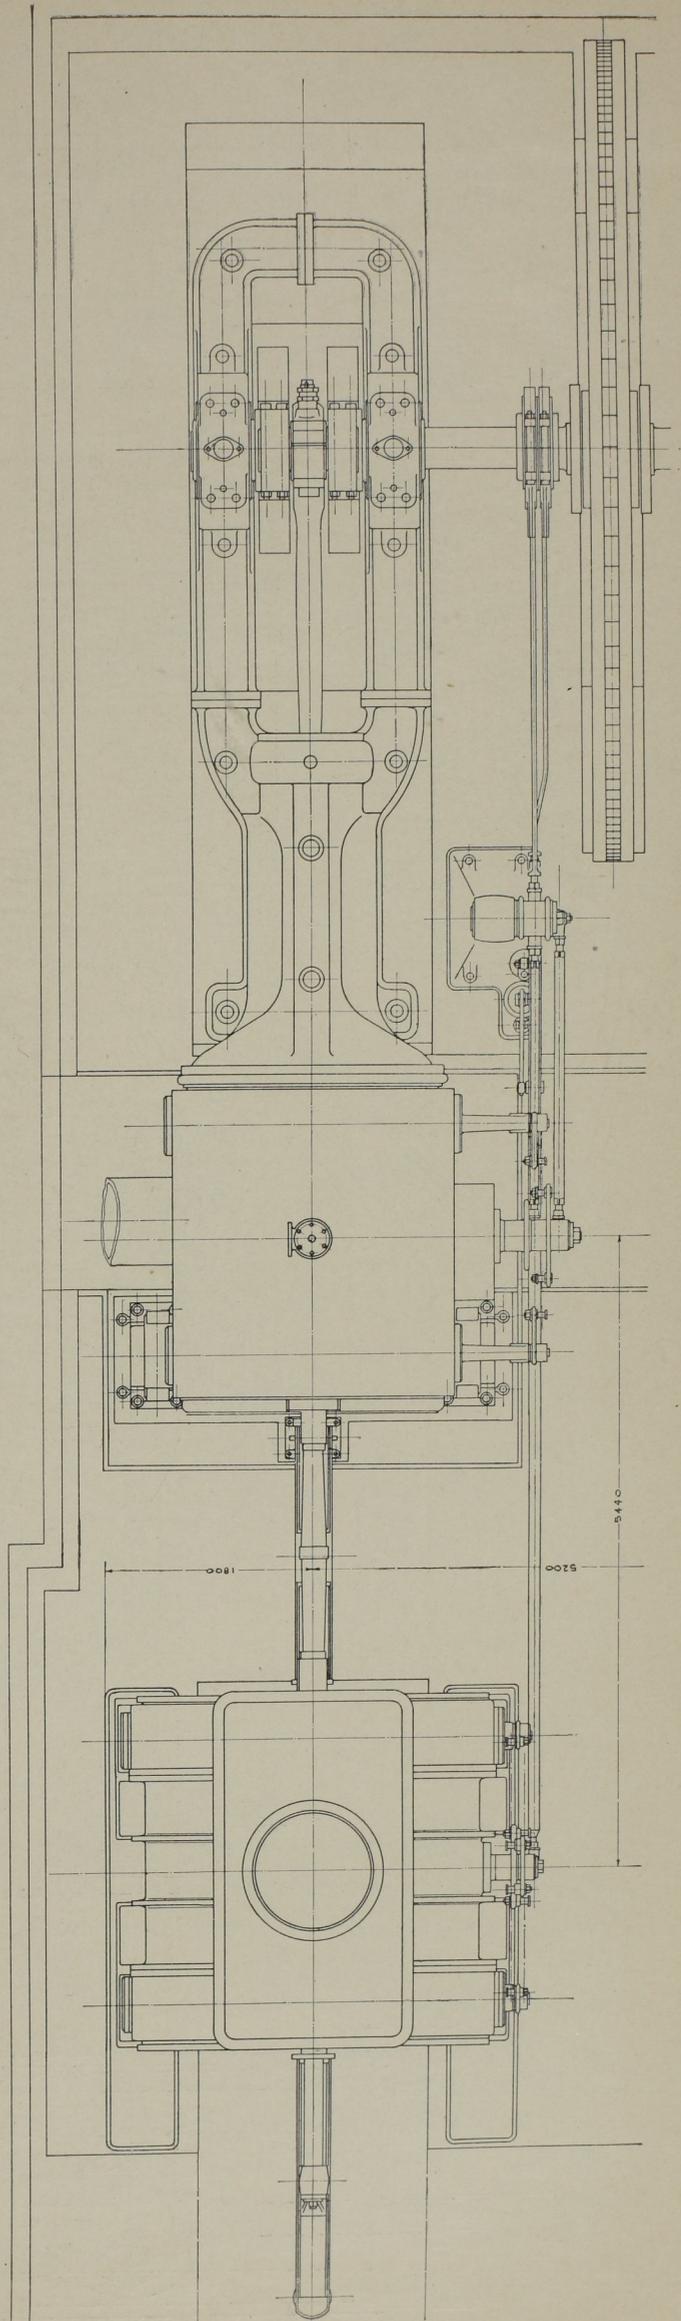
Grundriss der Niederdruckseite der Gebläsemaschine. Masst. 1 : 60.
